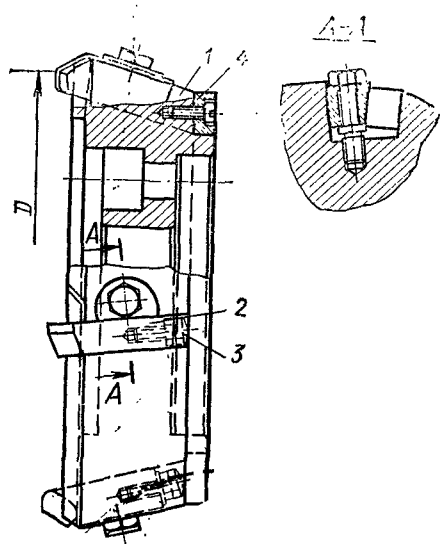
Торцовая фреза конструкции ВНИИ с заточкой ножей вне корпуса
